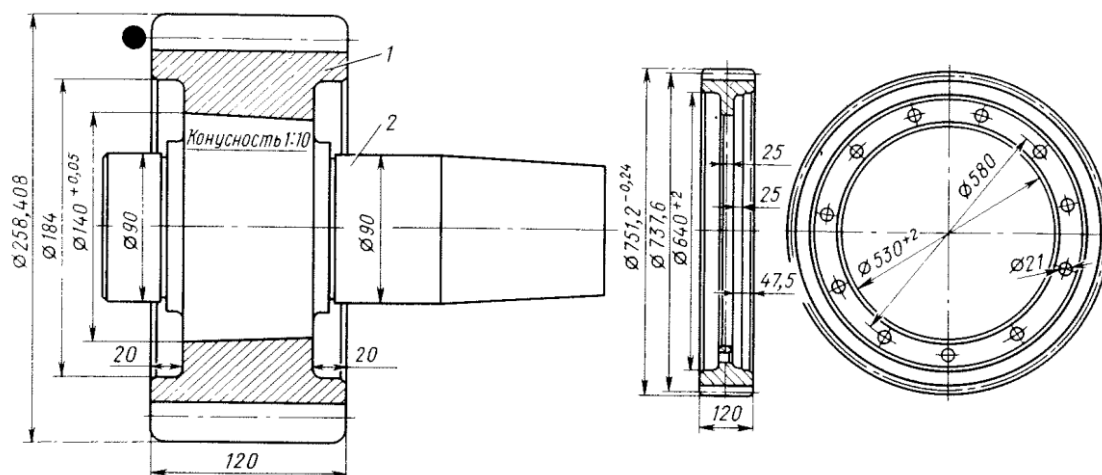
Малая шестерня и венец большого зубчатого колеса редуктора
